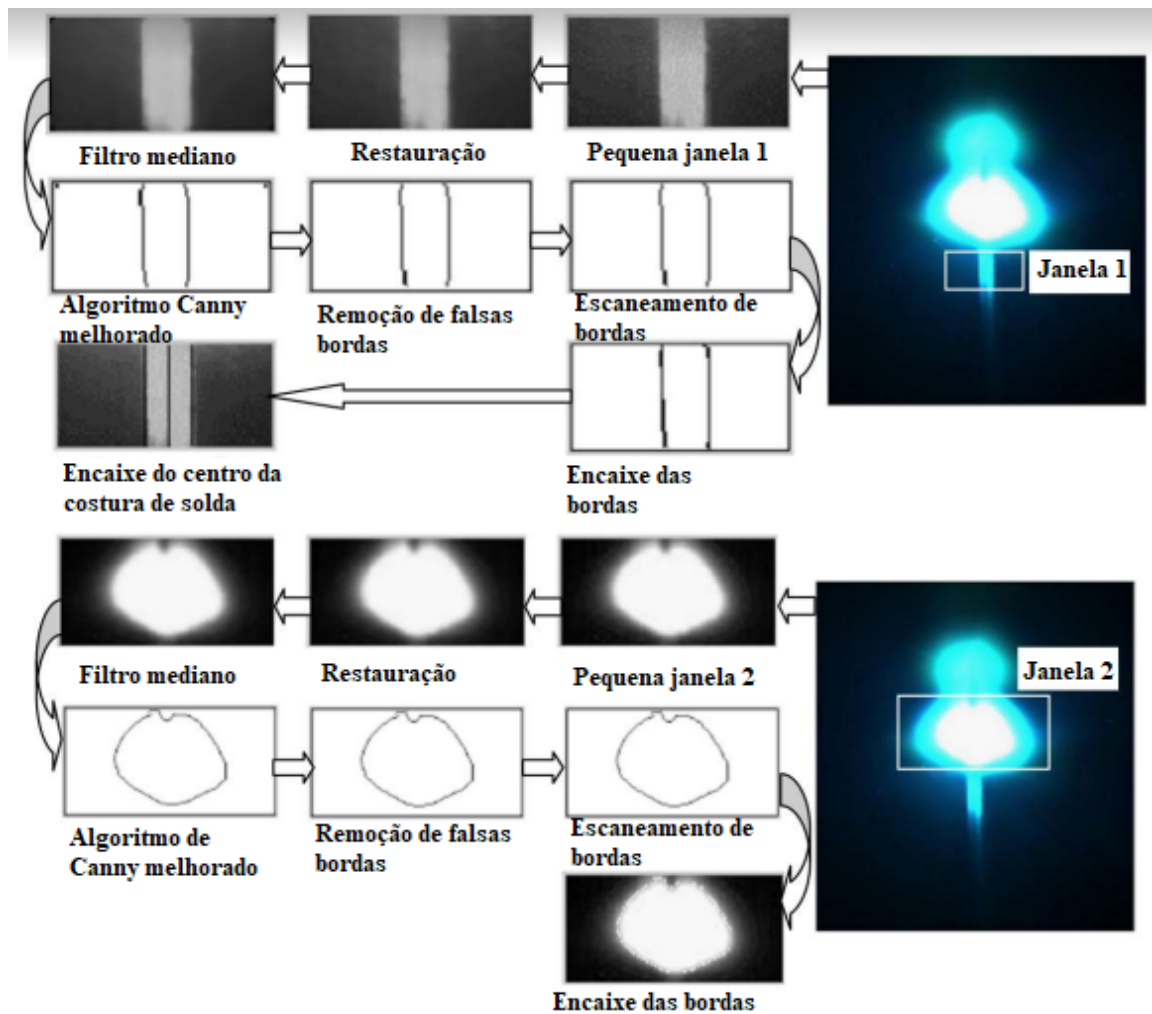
Fluxo do processamento de imagens durante a soldagem GMAW [105].
